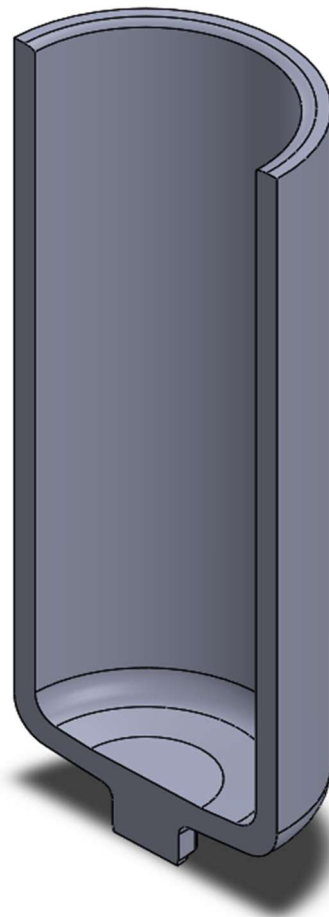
Vzory součástí vyráběné objemovým tvářením [5]
